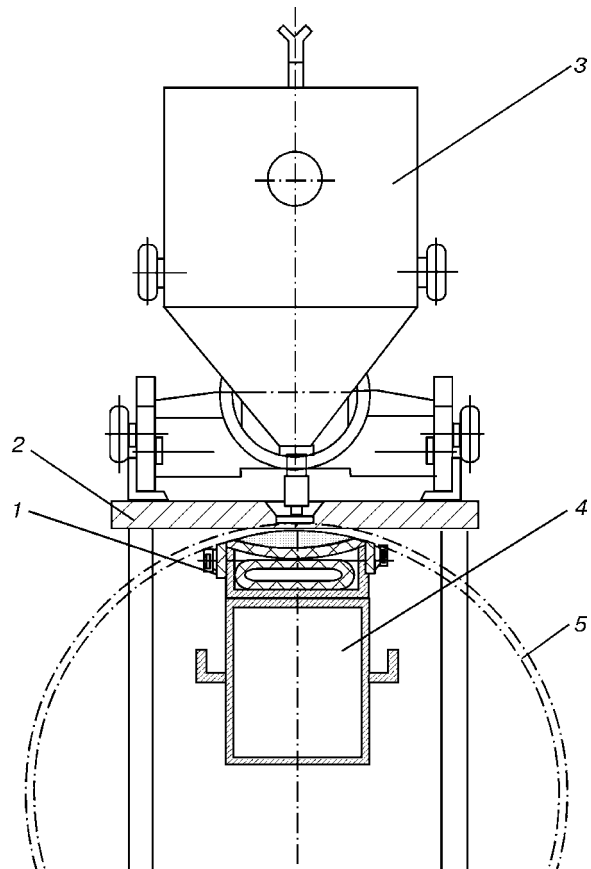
Схема установки для автоматической сварки под флюсом цилиндрических обечайек на флюсовой подушке: 1 — воздушный шланг; 2 — плита с направляющими; 3 — сварочный трактор; 4 — поворотная консоль с флюсовой подушкой; 5 — обечайка
